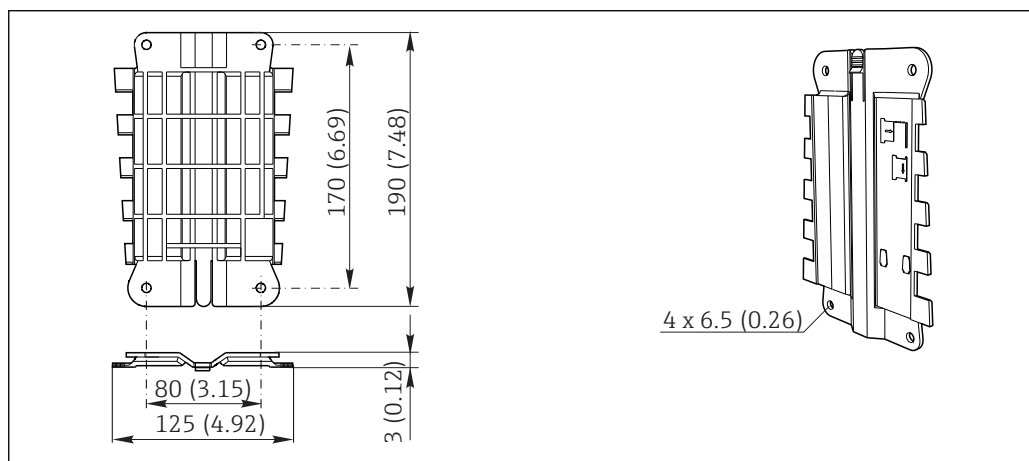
安装背板的外形尺寸示意图; 单位: mm (in)
